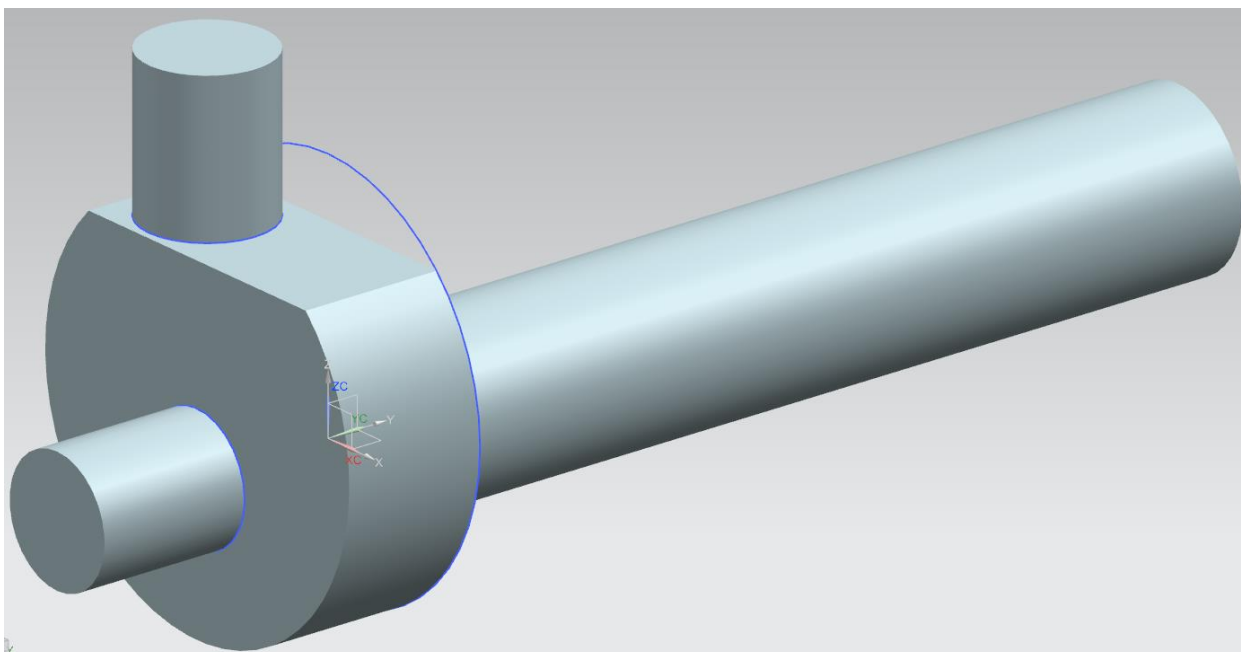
Внешний вид детали после создания патрубка выхода
